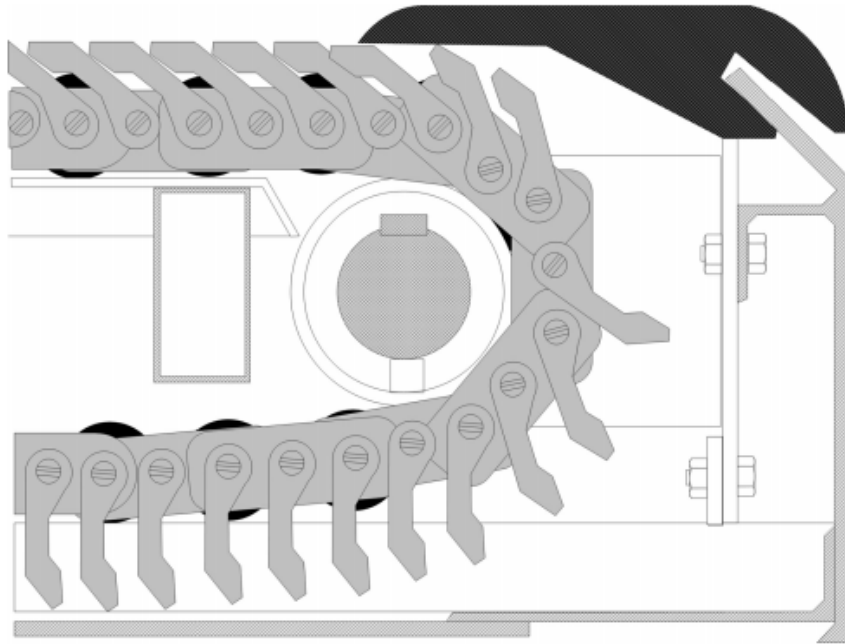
Principe technologique d'une grille de déplacement[11].
